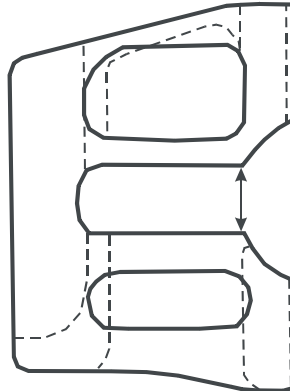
Aufweitversuch für U-Riegel- Anschlussköpfe
